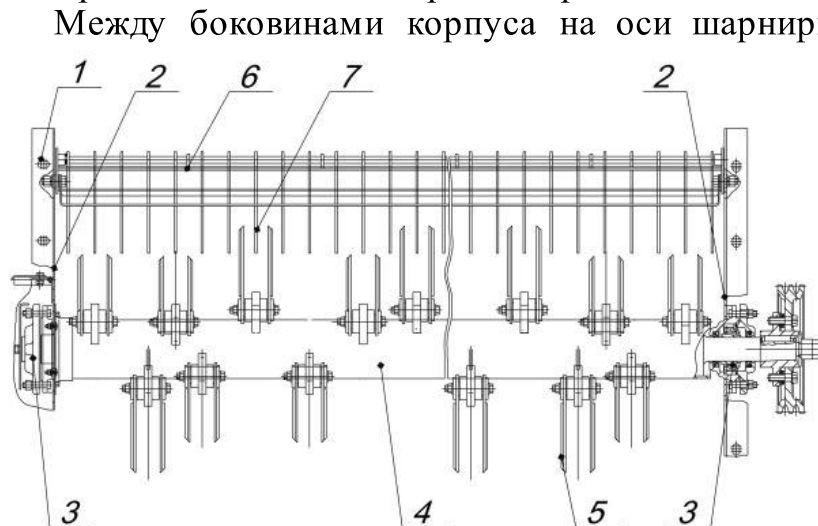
Соломоизмельчитель: 1 – корпус; 2 – боковина; 3 – подшипниковая опора; 4 – ротор; 5 – нож; 6 – ножевая опора; 7 – противорежущий нож
